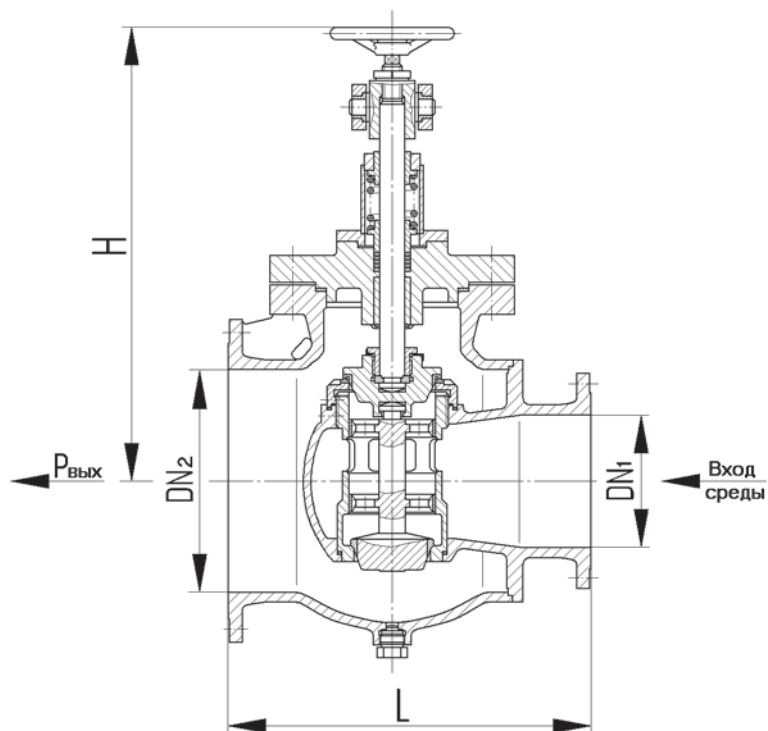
Клапан регулирующий проходной фланцевый с гидроприводом
